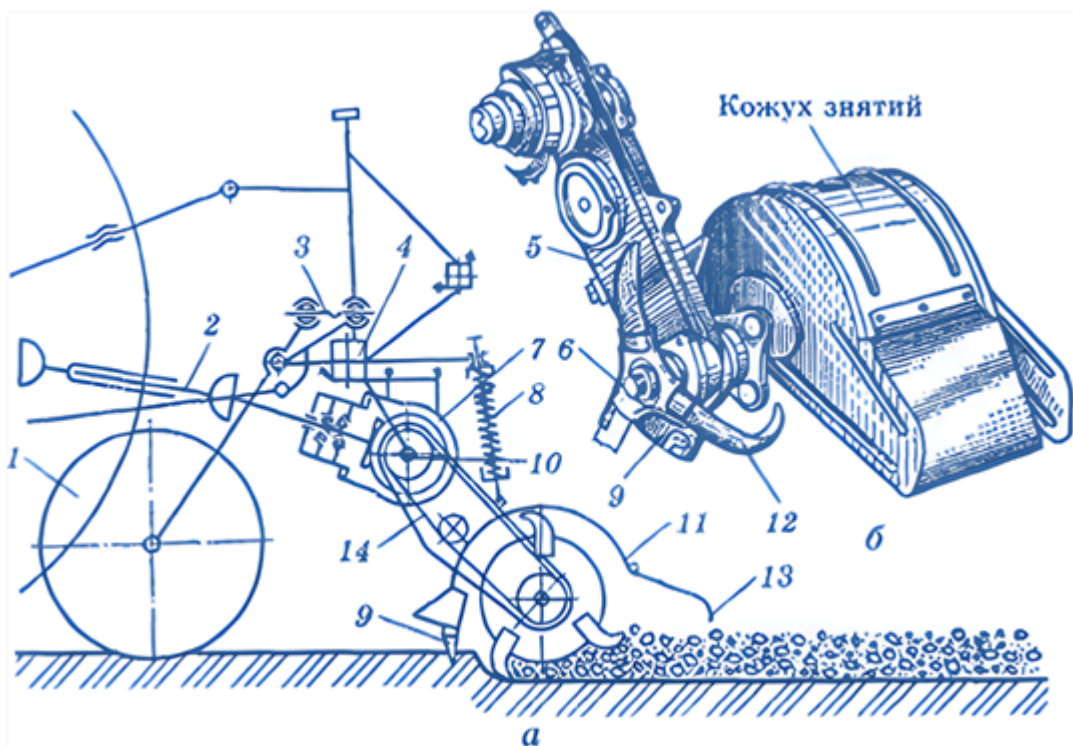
Культиватор фрезерний КФ-5,4:
